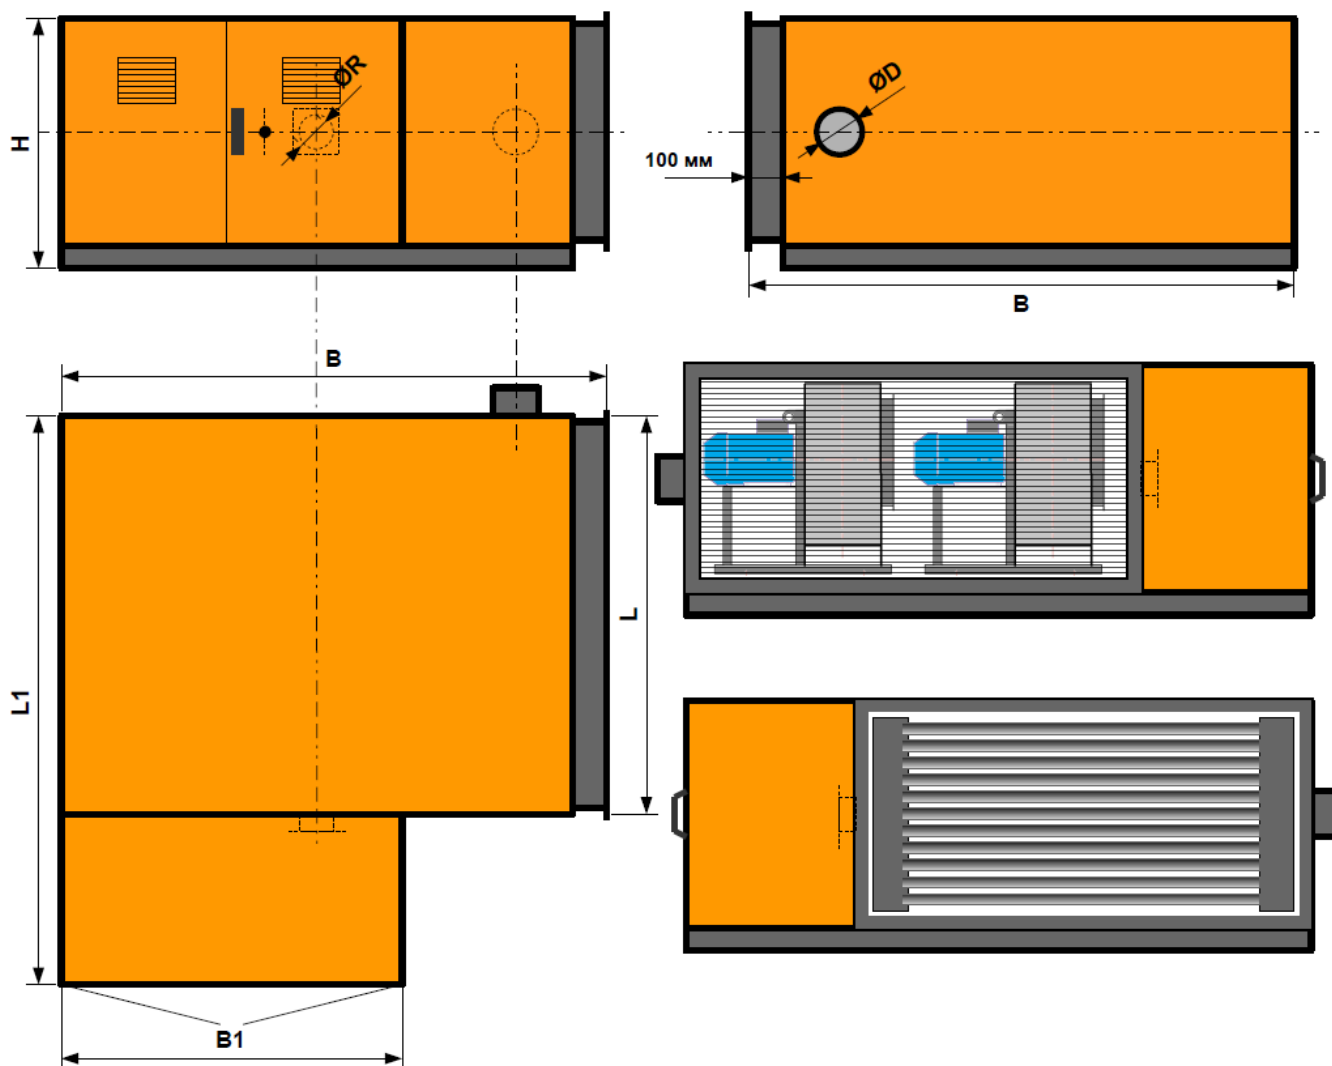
Габаритные размеры воздухонагревателей (теплообменников) серии HT-O
